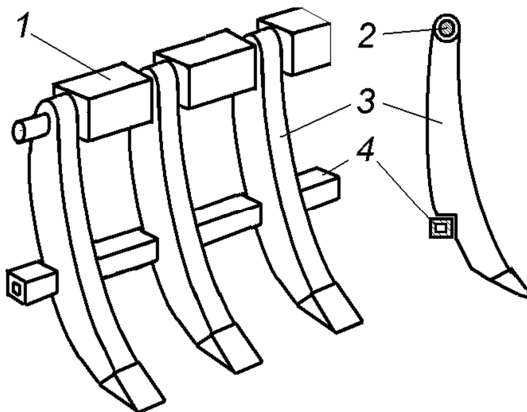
Крепление зубьев решётчатого отвала корчевателя – собираеля: 1– несущий брус; 2 – шарнир; 3 – корчующие зубья; 4 – опорный брус
